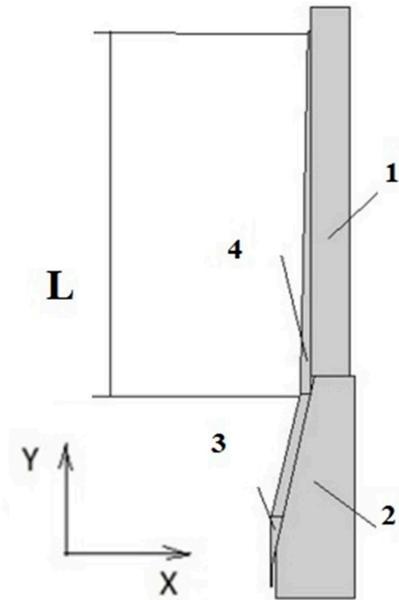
Схема зоны прохождения корочки заготовки: 1 – медная стенка; 2 – подвижный агрегат; 3 – очаг деформации; 4 – корочка; L – пояс формирования корочки заготовки
